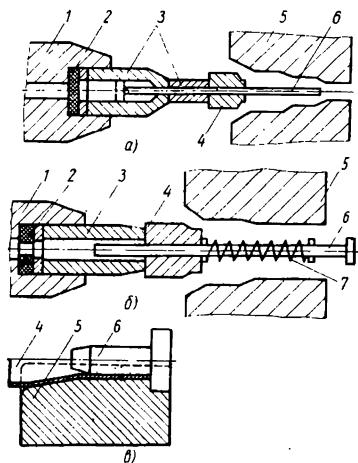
Установка оправок: а — в толкателе; б — в шпинделе; в — в бойках; 1 — подающее устройство; 2 — амортизирующие прокладки; 3 — толкатель; 4 — заготовка; 5 — бойки; 6 — оправка; 7 — пружина
